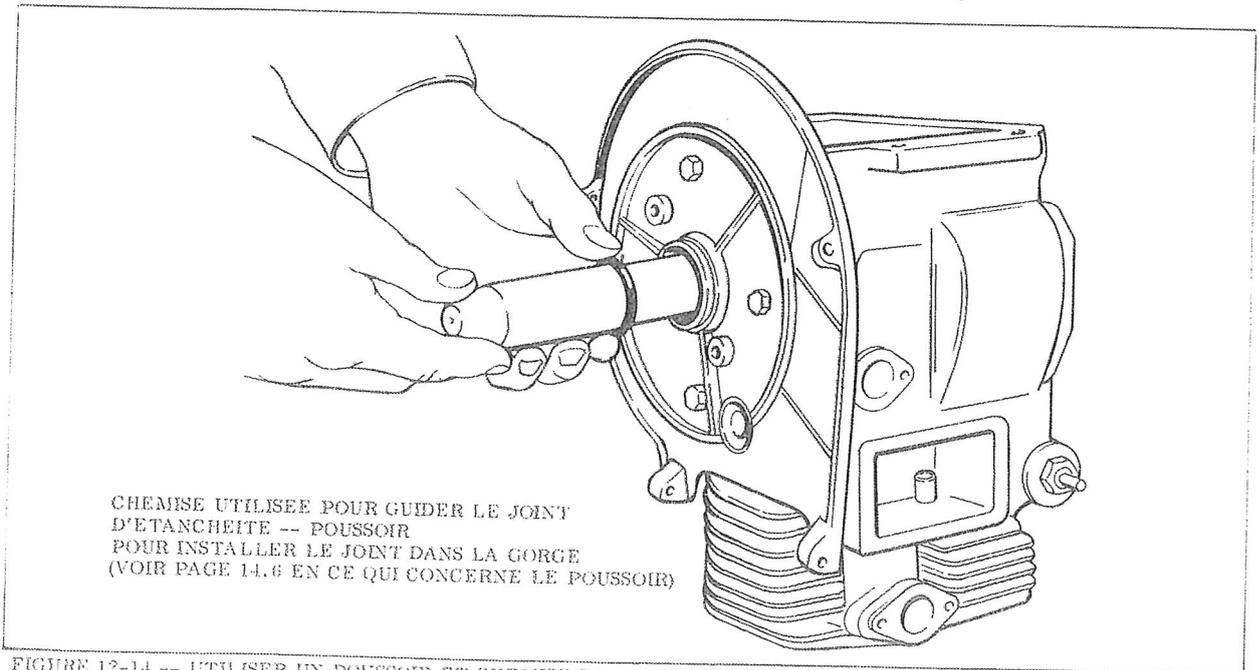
UTILISER UN POUSSOIR ET CHEMISE DE JOINT POUR INSTALLER LE JOINT D'ETANCHEITE AVANT.
